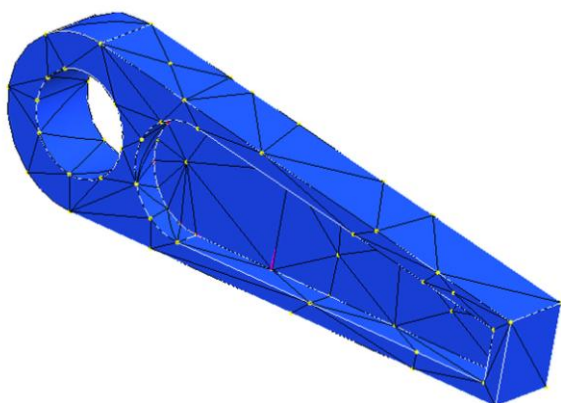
„*Detailed Fillet Modeling*“ zapnuto
